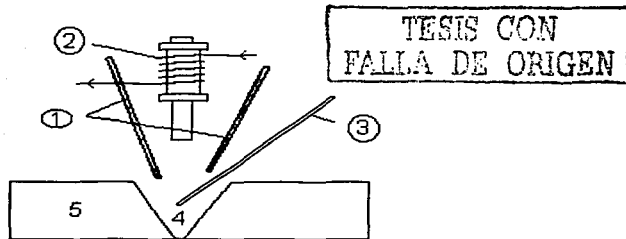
Soldadura por arco soplado (Método Zerener) [1]
